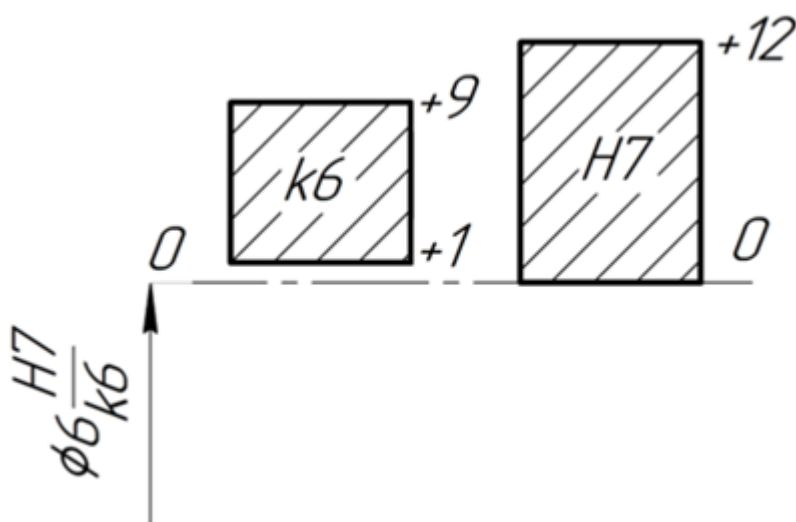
Посадка внешнего кольца шарикоподшипников с подшипниковой втулкой.
